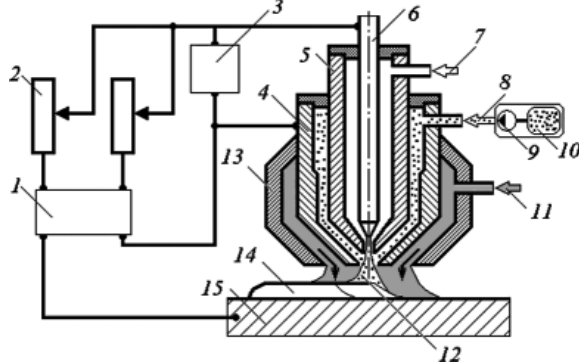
Схема плазмово-порошкового наплавлення: 1 – джерело струму; 2 – реостат; 3 – осцилятор; 4 – фокусуюче сопло; 5 – плазмове сопло; 6 – електрод; 7 – подача плазموутворювального газу; 8 – подача транспортувального газу спільно з порошком; 9 – компресор; 10 – порошковий накопичувач; 11 – подача захисного газу; 12 – плазма; 13 – захисне сопло; 14 – наплавлений валик; 15 – основний метал деталі
